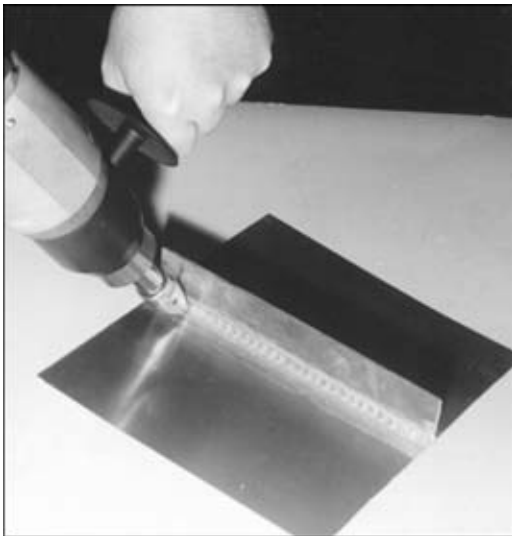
Высокочастотная проковка фрагмента сварного соединения, выполняемая ручным инструментом
